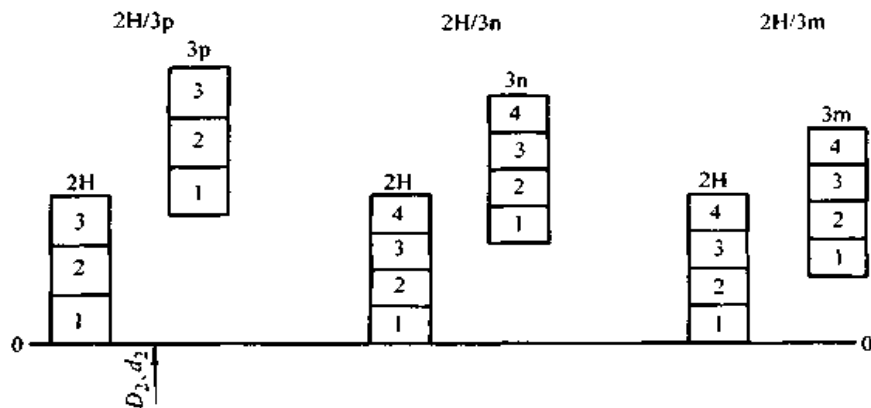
过盈配合螺纹中径公差带分组位置
